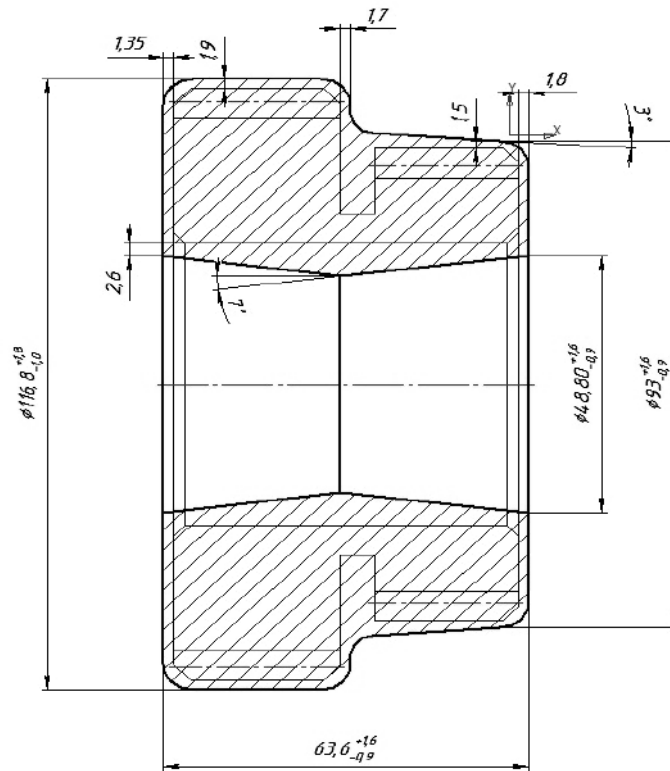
Заготовка сателіту з визначеними припусками та допусками
